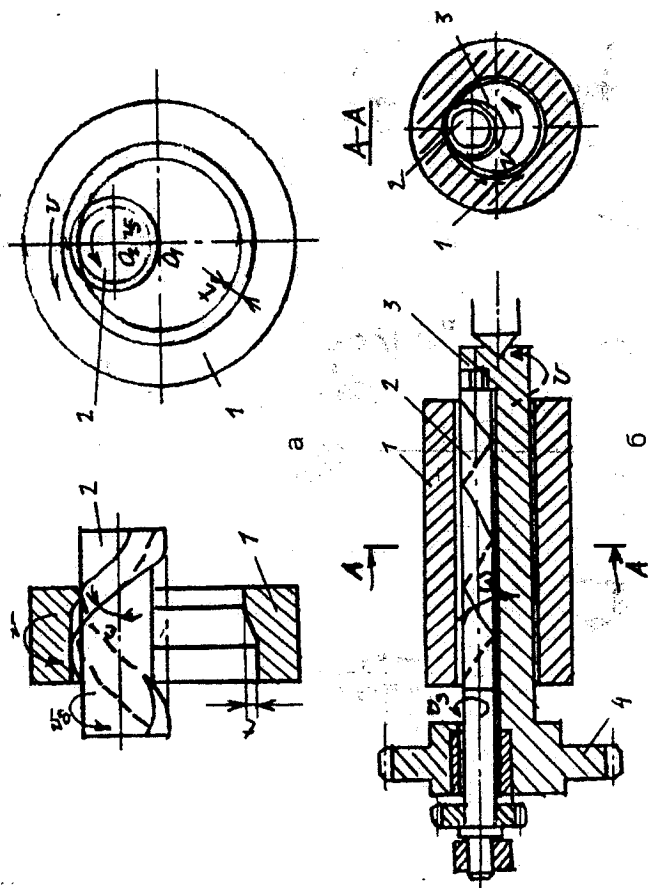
Розточування гвинтовими різцями обертової деталі (а),
